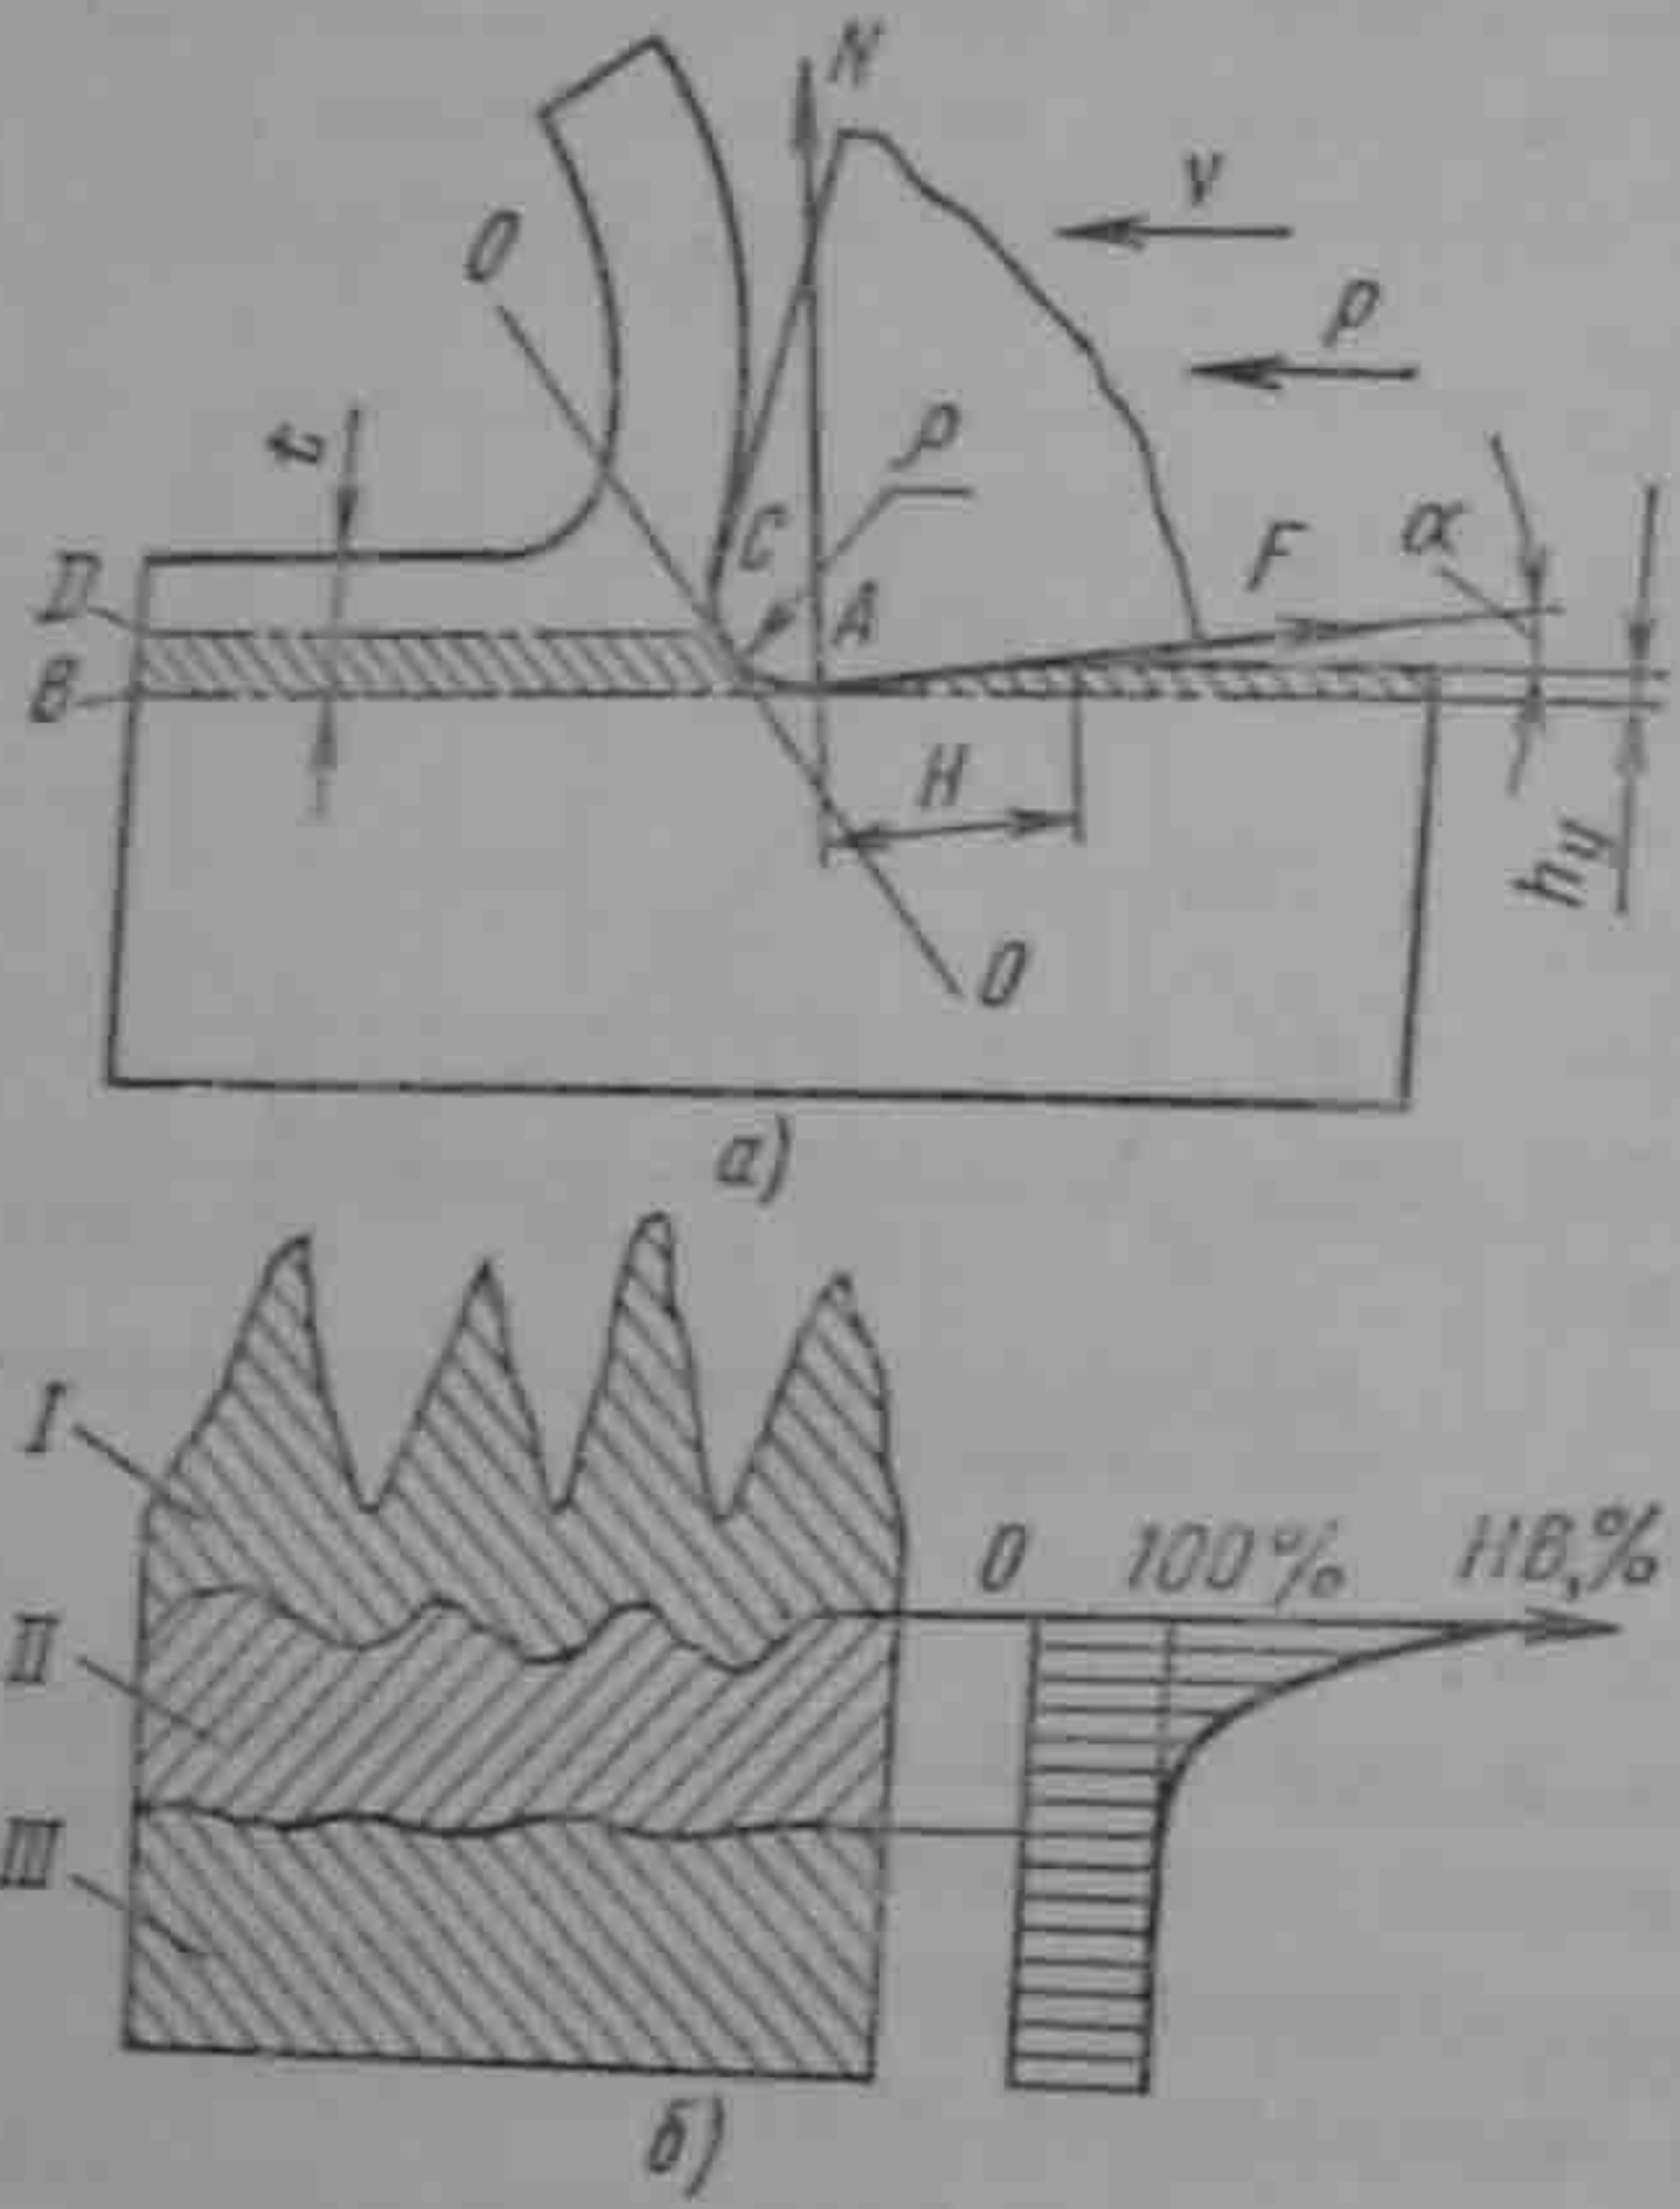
Схема образования поверхностного слоя заготовки (а) и вид распространения упрочнения по толщине заготовки (б)
